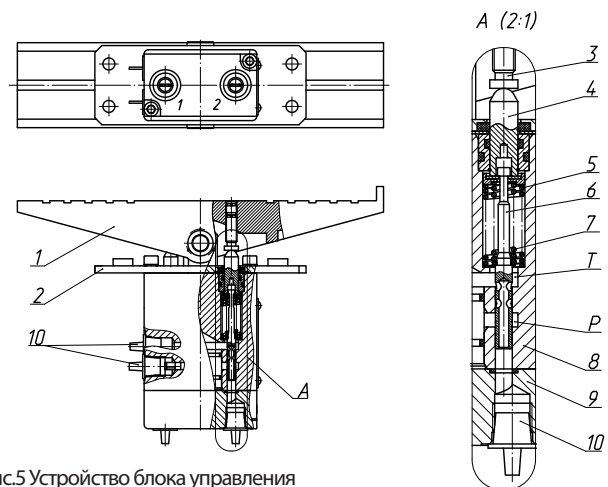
Устройство блока управления 1–педаль, 2–опора, 3–упор, 4–толкатель, 5–пружина возвратная, 6–золотник, 7–пружина регулировочная, 8–корпус, 9–плита, 10–заглушка
